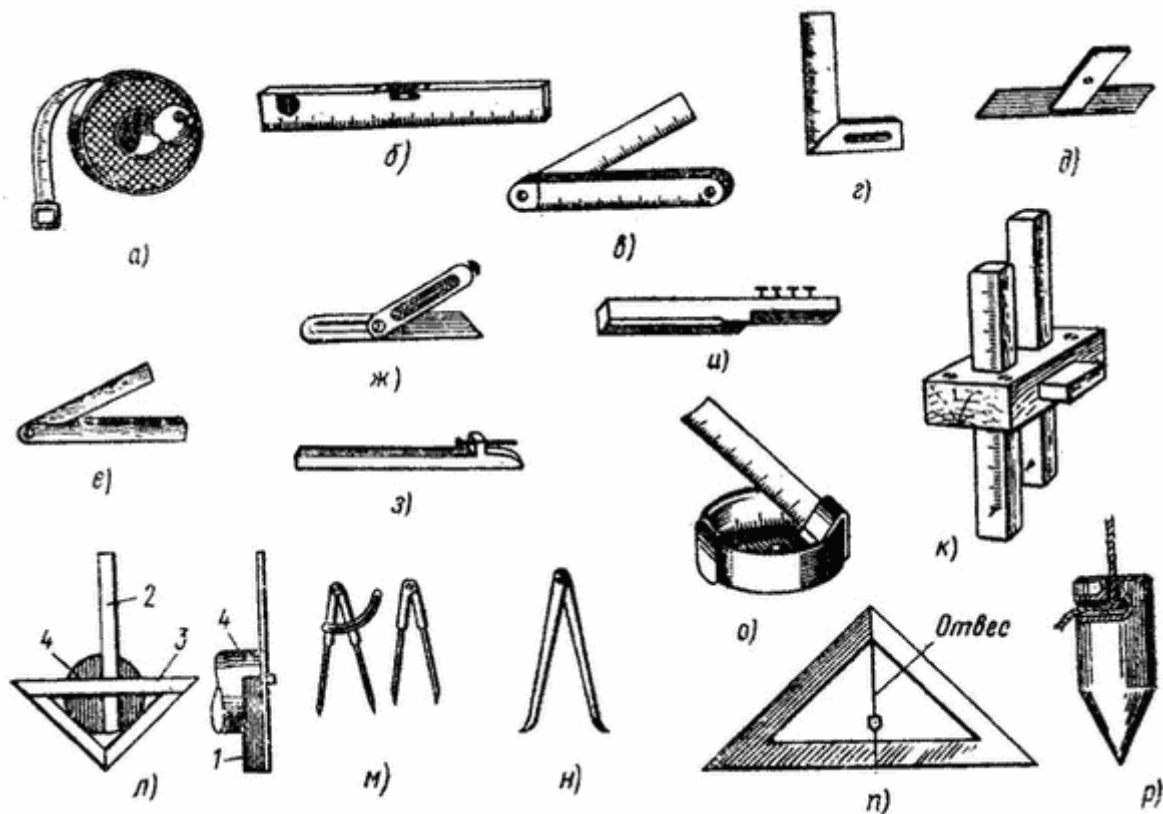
Инструмент для измерения и разметки: а — рулетка; б — уровень; в — складной метр; г — угольник; д — ерунок; е — деревянная малка; ж — металлическая малка; з — отволока; и — скоба; к — рейсмус; л — угольник - центроискатель; м — циркуль; н — нутромер; о — метр-рулетка; п — уровень с отвесом; р — отвес.
